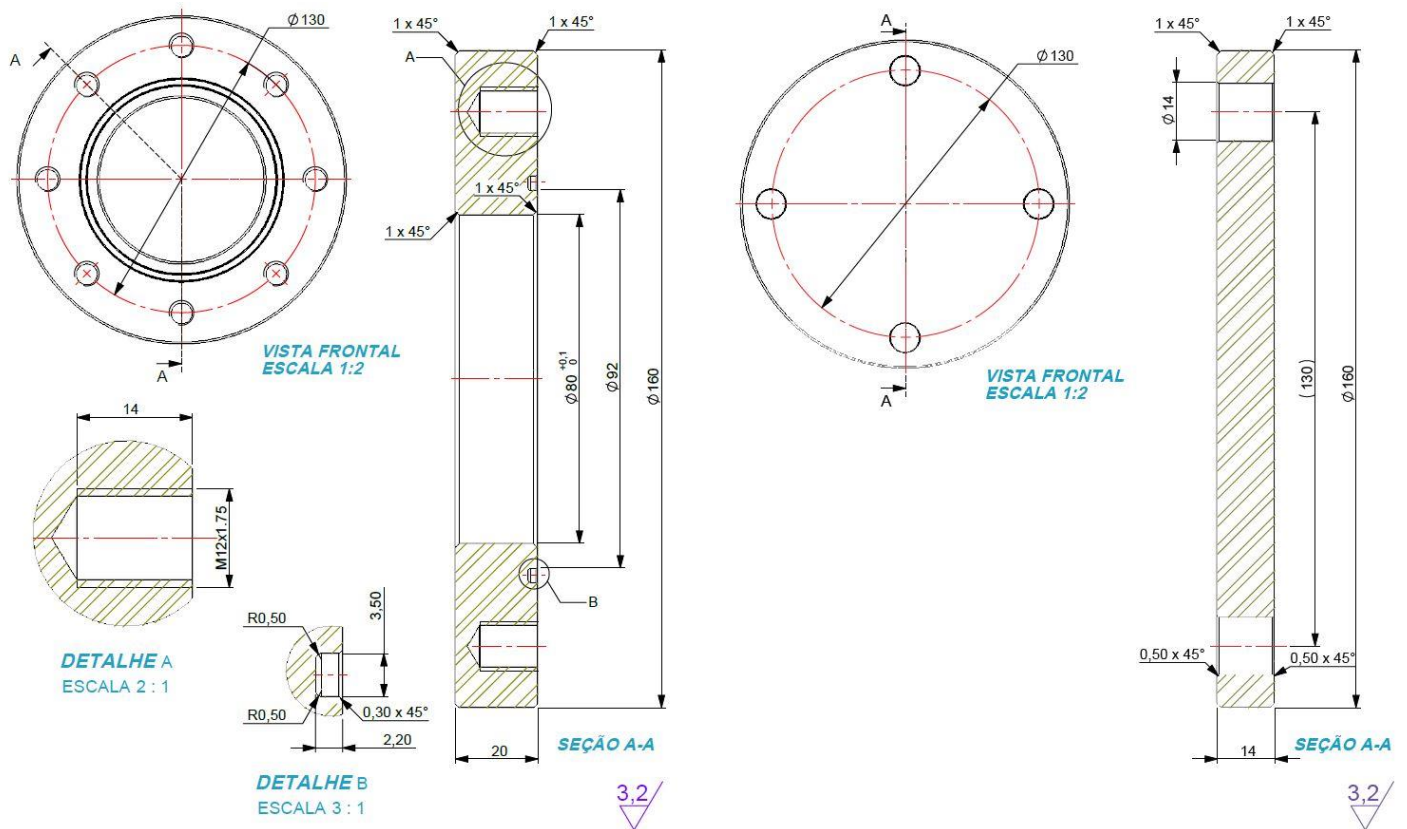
Dimensionamento para montagem do Flange (Cotas em milímetro).
